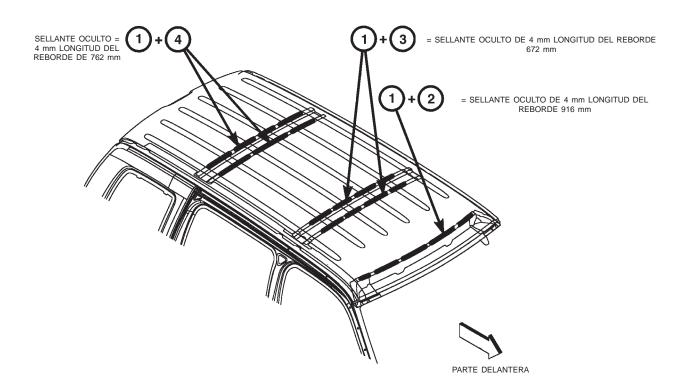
CONJUNTO DE PLANCHA DE TECHO
